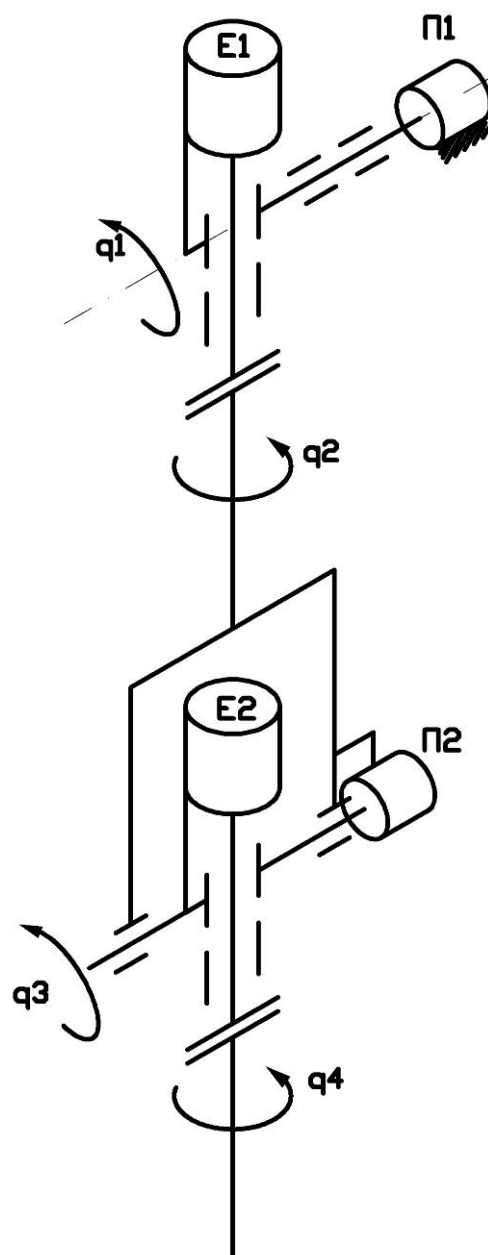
б. Кінематичний кресленик стенда-імітатора верхньої кінцівки
